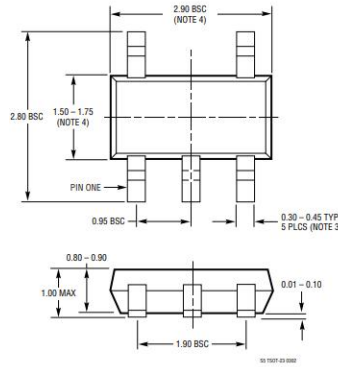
Габаритні розміри контролера заряду LTC4054
